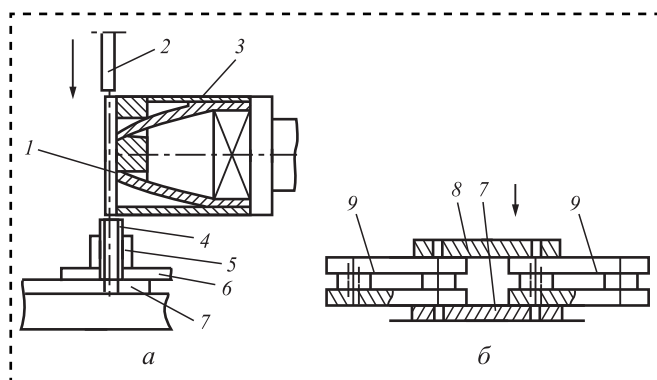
Схемы запрессовки оси в отверстие нижней соединительной пластины отрезка ВРЦ (а) и напрессовки верхней соединительной пластины на оси катушек отрезка ВРЦ (б): 1 — ось на магнитном шиберном захвате 3; 2 — пуансон прессы; 4 — втулка, запрессованная в нижнюю пластину б катушки; 5 — ролик; 7 — нижняя соединительная пластина отрезка ВРЦ; 8 — верхняя соединительная пластина; 9 — катушка ВРЦ
